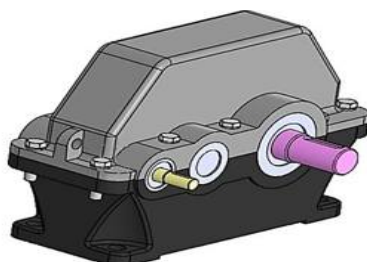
3D-модель двухступенчатого цилиндрического редуктора
